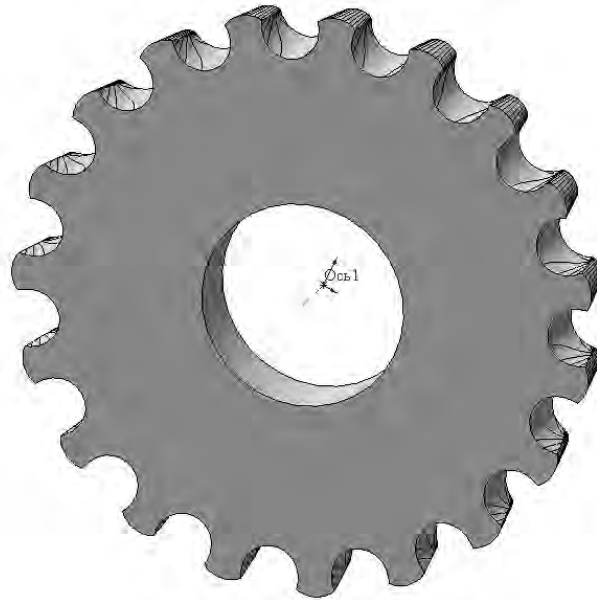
Компьютерная модель сателлитного колеса прецессионной роликовой передачи
